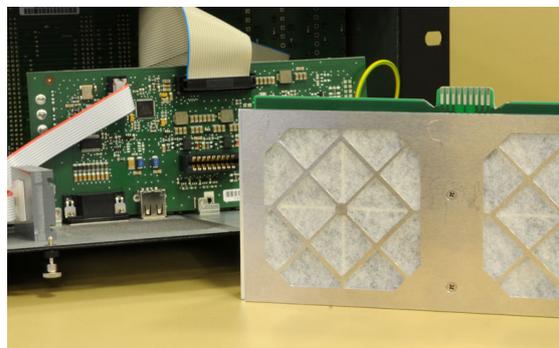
Lösen der Befestigungsschrauben der Frontplatte
